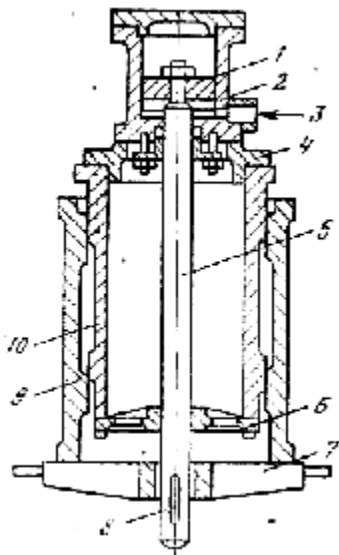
Приспособление для запрессовки гильзы в цилиндр:
